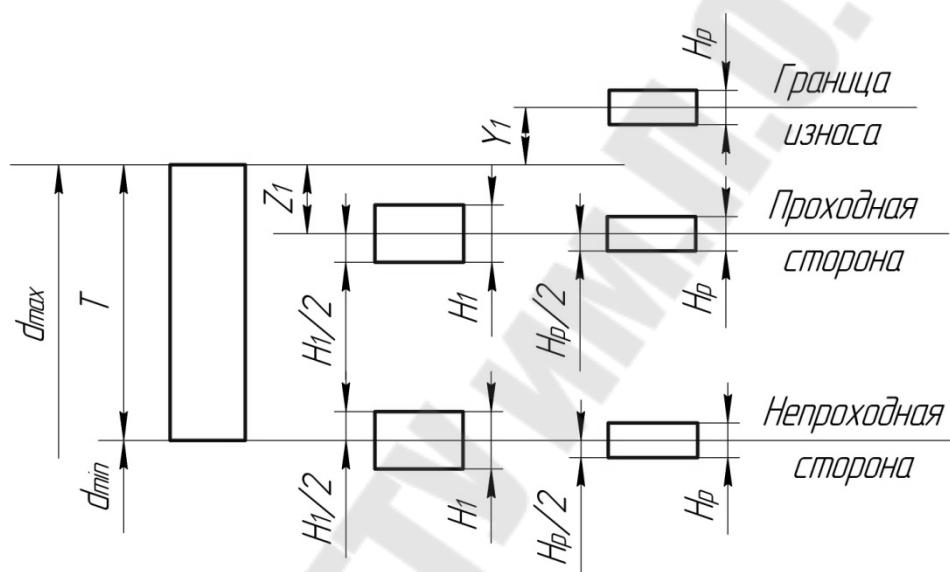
Схема расположения полей допусков калибров-скоб
